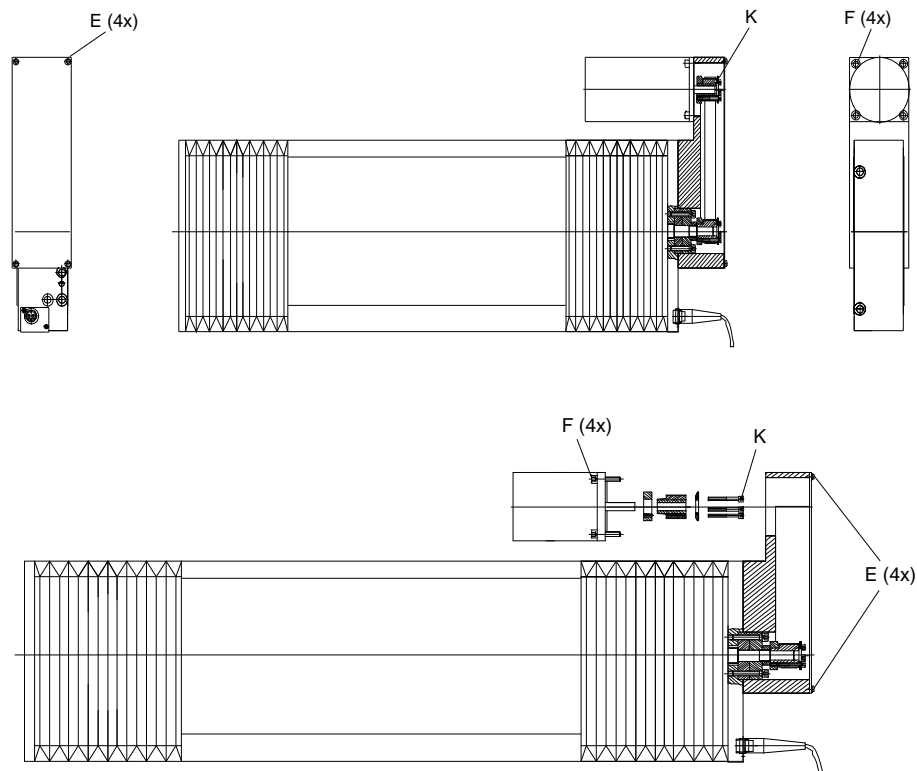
Motor bei abgewinkeltem Motoranbau wechseln
